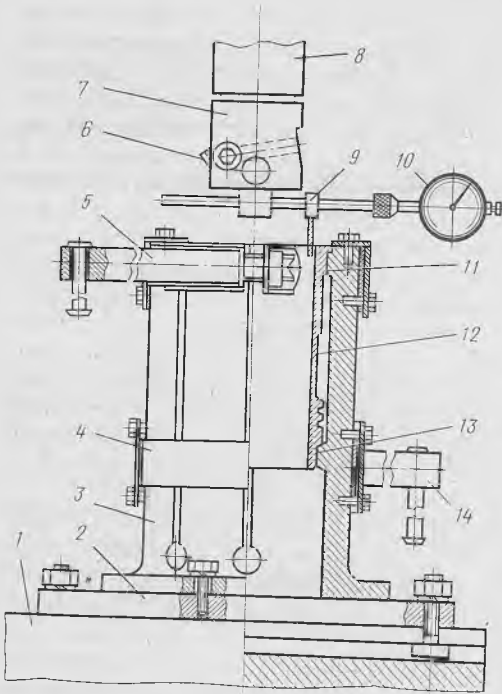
Приспособление для центровки и закрепления гильзы цилиндров на столе расточного станка:
